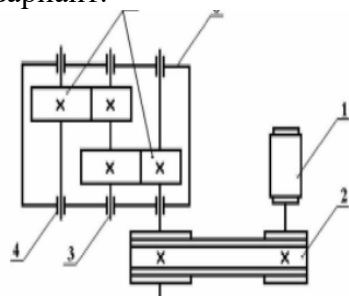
Кинематическая схема привода с цилиндрическим зубчатым редуктором
